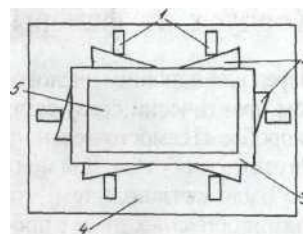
Шаблон для сборки корпусов: 1 — упоры (6 шт.); 2 — клинья (6 шт.); 3 — подготовленный к сколачиванию корпус; 4 — основа шаблона; 5 — плато по внутреннему размеру корпуса (450x375 мм)
